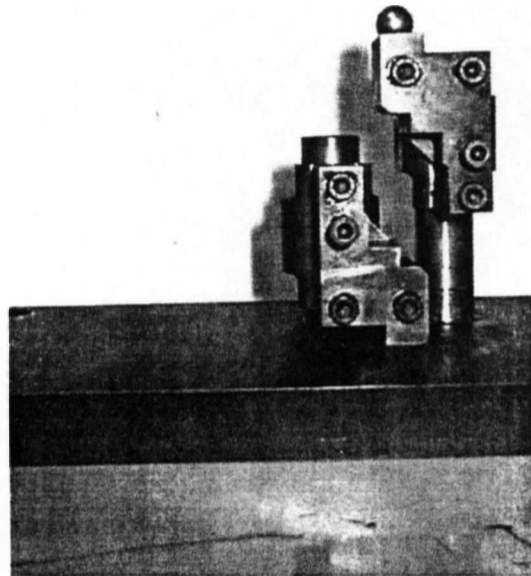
Dispositivo para ensaio de cisalhamento.
